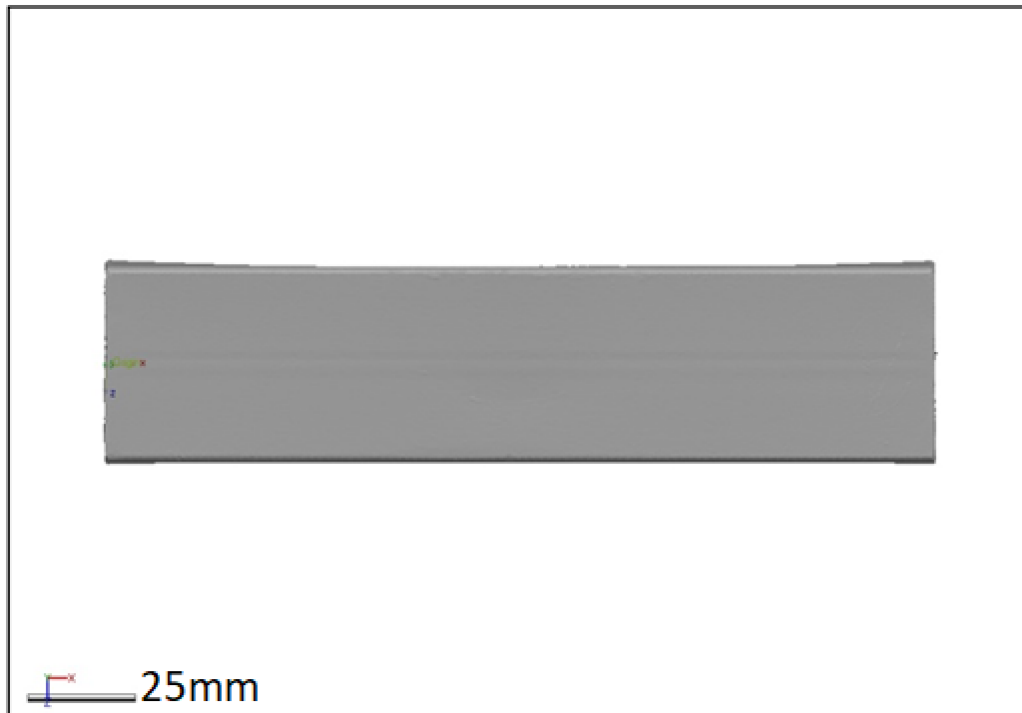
Vista Lateral do perfil retangular após Ensaio nas condições de Ensaio 8
